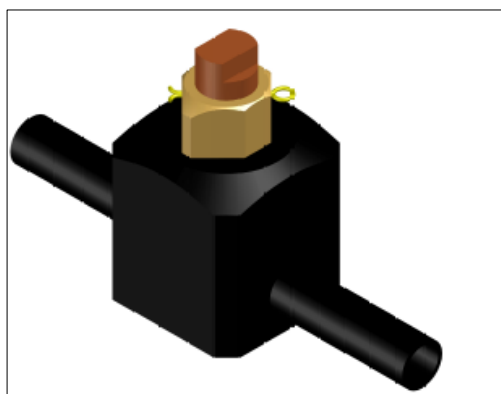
Válvula com dispositivo para tubo guarda (tulipa).
